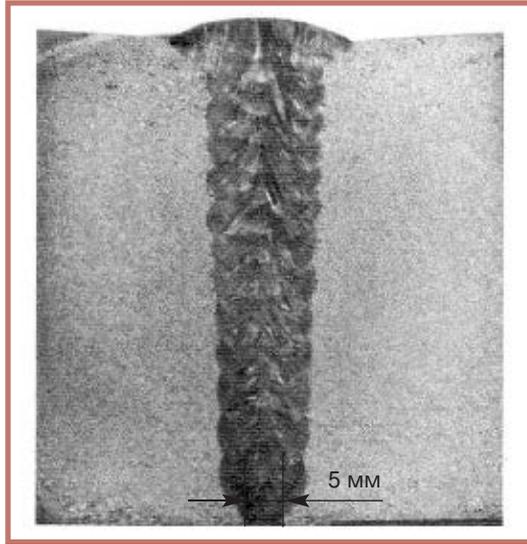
Макрошлиф поперечного сечения многопроходного сварного шва на стальной трубе с толщиной стенки 50 мм (ТИГ сварка в узкую разделку кромок, фирма «Hitachi», Канагава, Япония)
